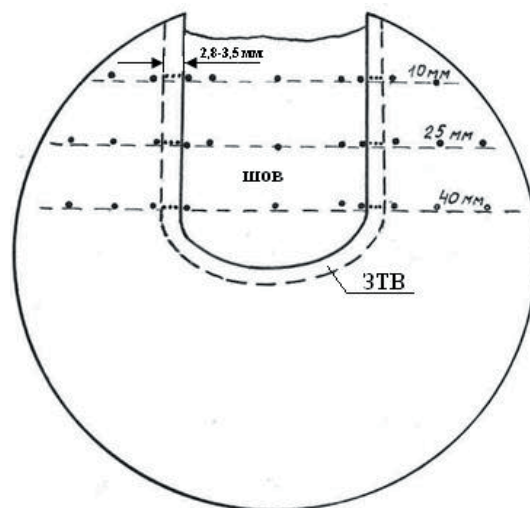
Схема измерения твердости HV₅ сварных соединений стали, выполненных сваркой способом поперечной горки
